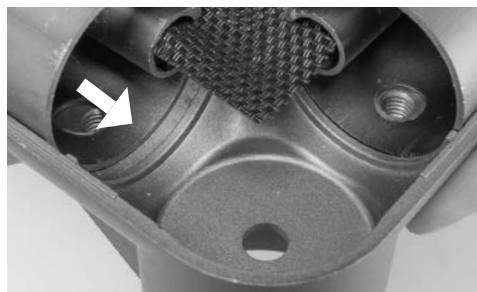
Guider les tubes jusqu'à la butée
